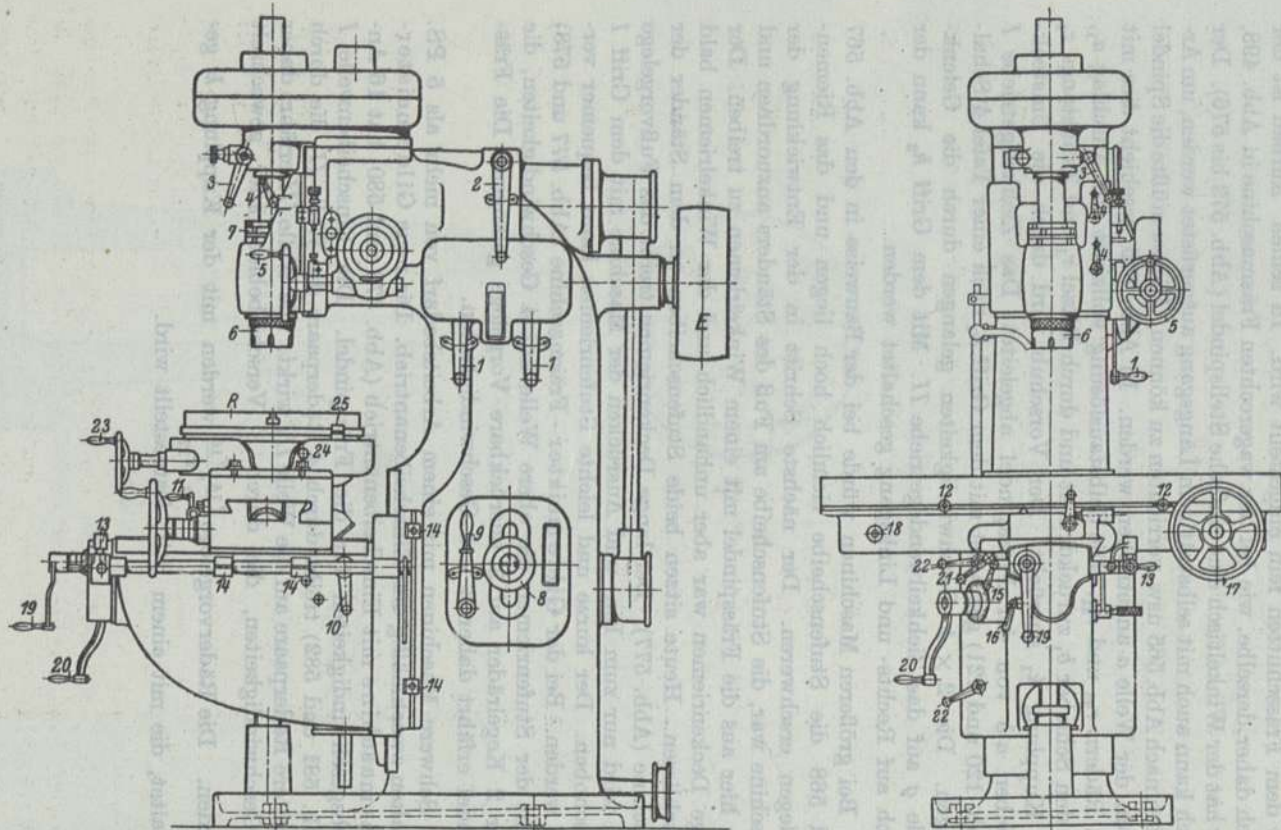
und 580. Senkrechte Fräsmaschine von Gildemeister & Co., A. G., Bielefeld.
